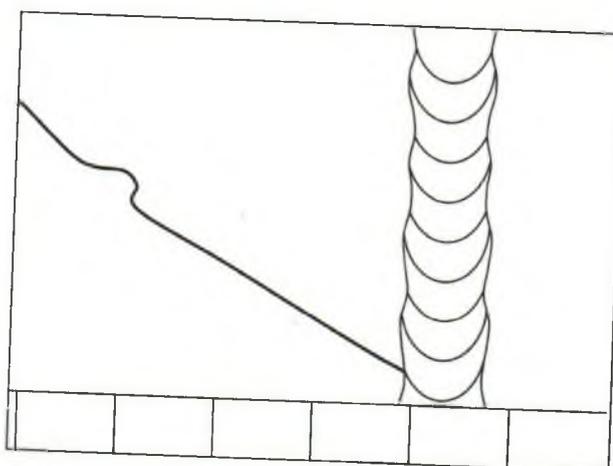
Закат – прикатанный продольный выступ – в основном металле трубы, выходящий на кромку детали в стыковом сварном соединении трубопровода
